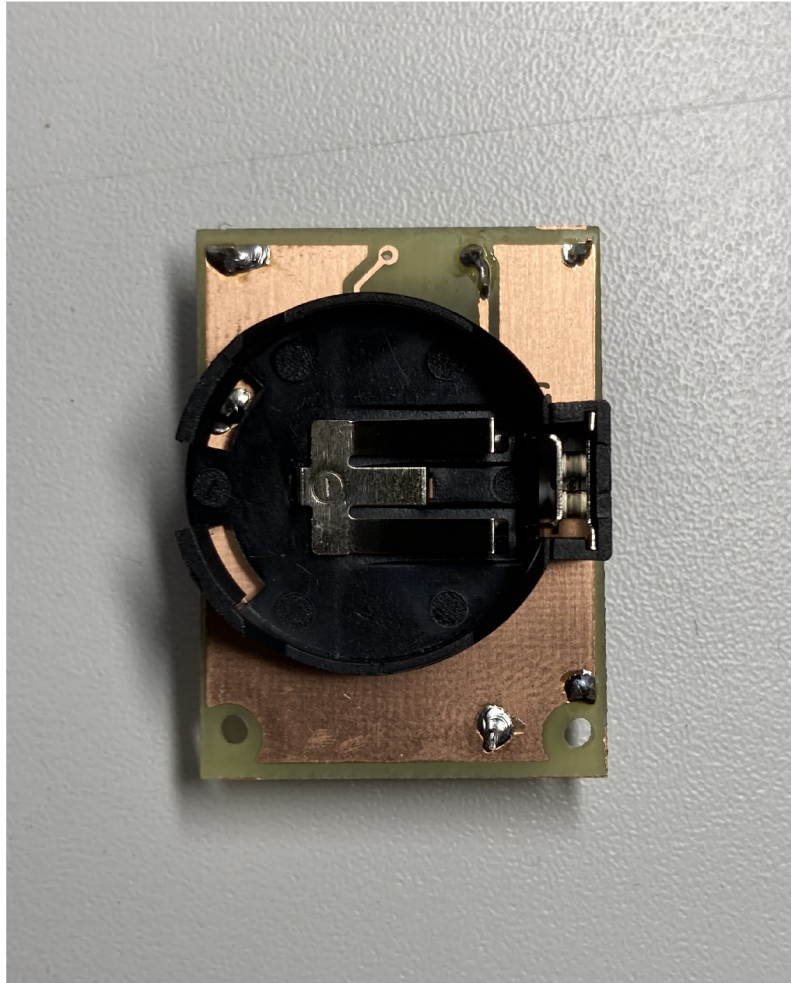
Spodní strana desky plošných spojů pomocné desky pro měření.
